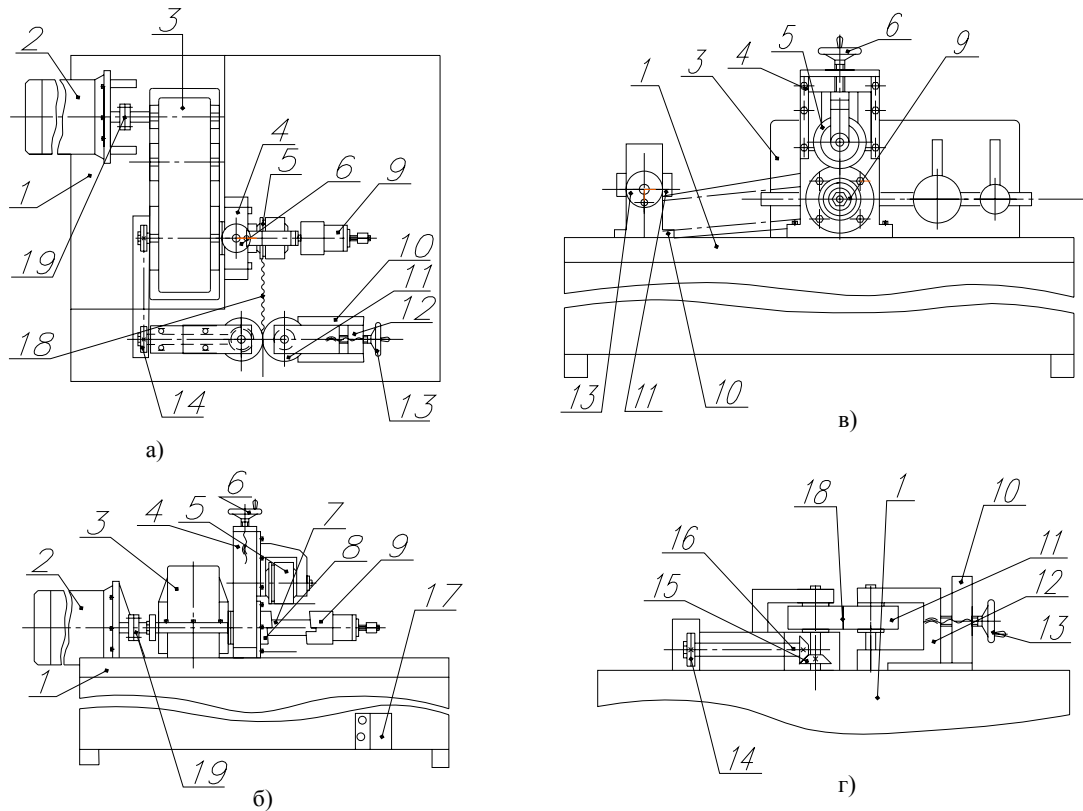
Верстат для виготовлення гвинтових гофрованих заготовок
